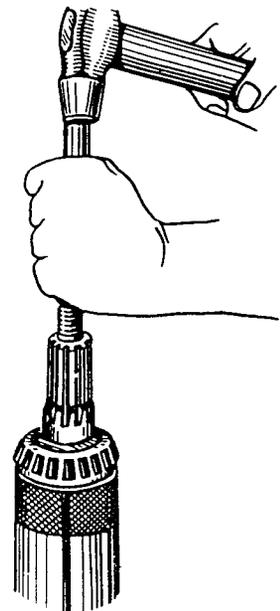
Ausbau des hinteren Lagers aus dem Antriebsrad
